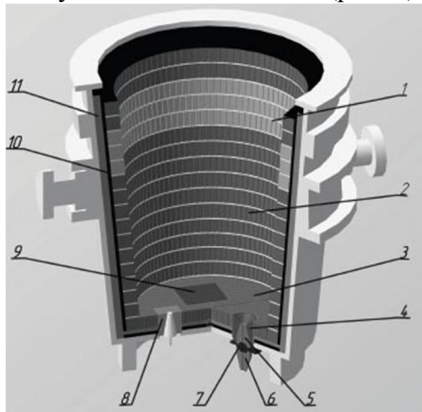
Схема футеровки сталеразливочного ковша: 1 – шлаковый пояс; 2 – рабочий слой стен ковша; 3 – днище ковша; 4 – гнездовой блок; 5 – верхний стакан разливочного узла; 6 – нижний стакан разливочного узла; 7 – шиберный затвор; 8 – продувочный узел с гнездовым блоком; 9 – бойное место; 10 – набивочная масса; 11 – защитный стол
